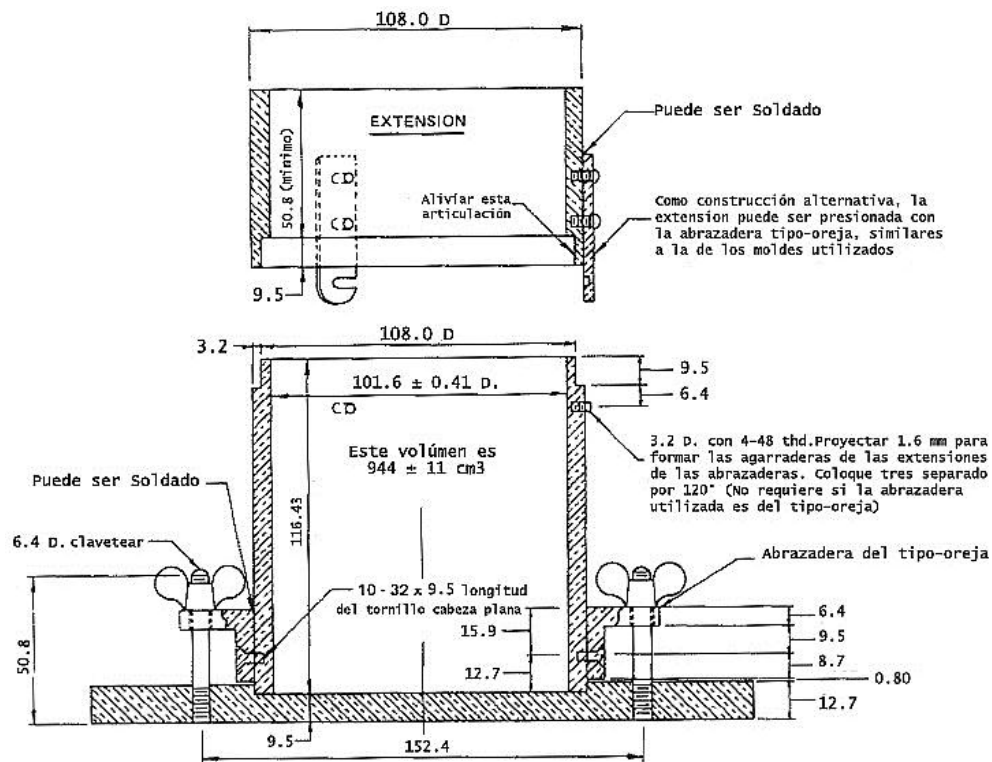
Moldes Cilíndricos para Suelo Cemento (dimensiones en mm)
